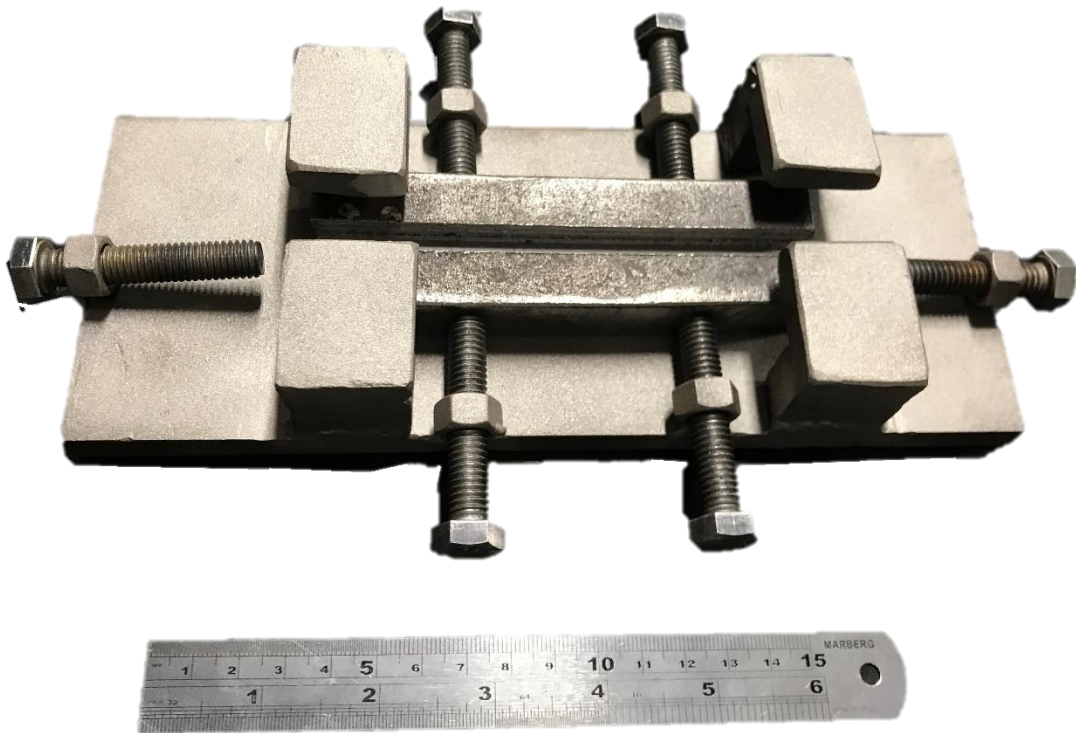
Posicionador dedicado para o corpo de prova utilizado neste trabalho. Garante o bom posicionamento e evita abertura entre as partes a serem soldadas.
